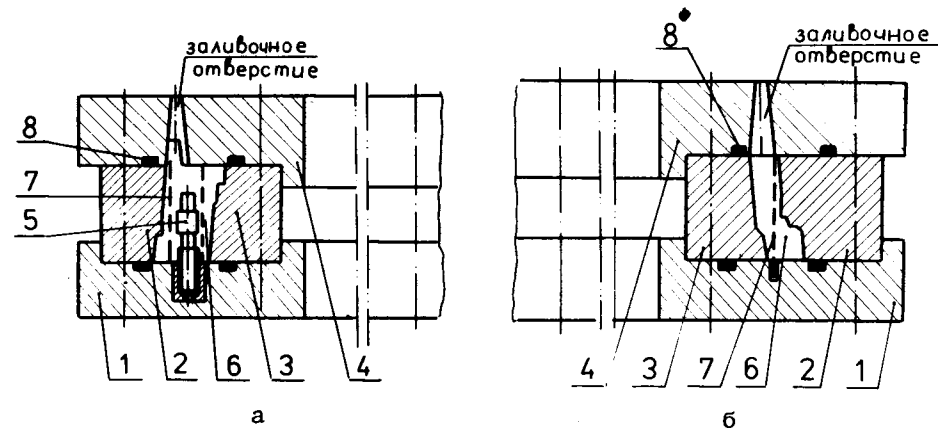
Прессформы для отливки колец: а - для катодных, б - для анодных проволочек. 1 - основание; 2 - наружное формирующее кольцо; 3 - внутреннее формирующее кольцо; 4 - крышка; 5 - винт и втулка; 6 - кольцо /отливка/; 7 - полоска перфорированного стеклотекстолита; 8 - уплотнительные кольца.
